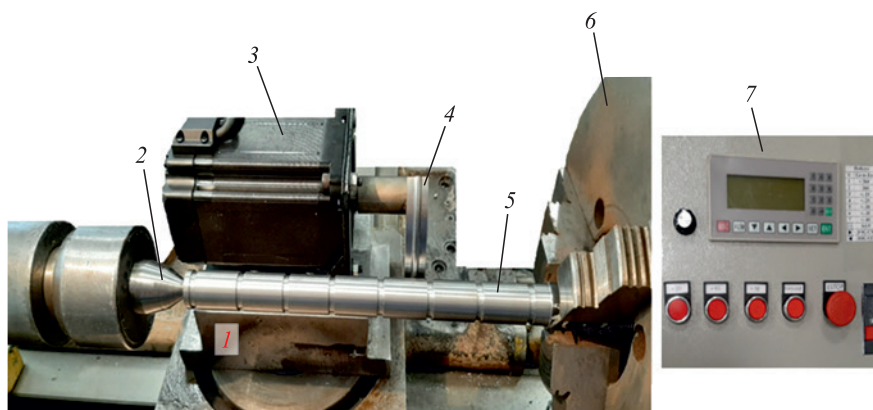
Общий вид устройства для маятникового ППД наружных поверхностей цилиндрических деталей:
